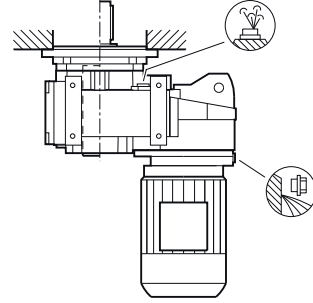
Yassı dişli için montaj konumları F.AD Geçmeli model Boyutlar 39 - 89
